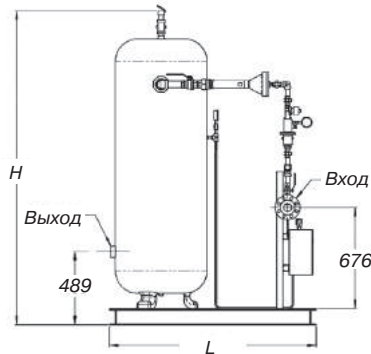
Габаритные размеры установки испарительной Metan-3-3-140(-400)-B
